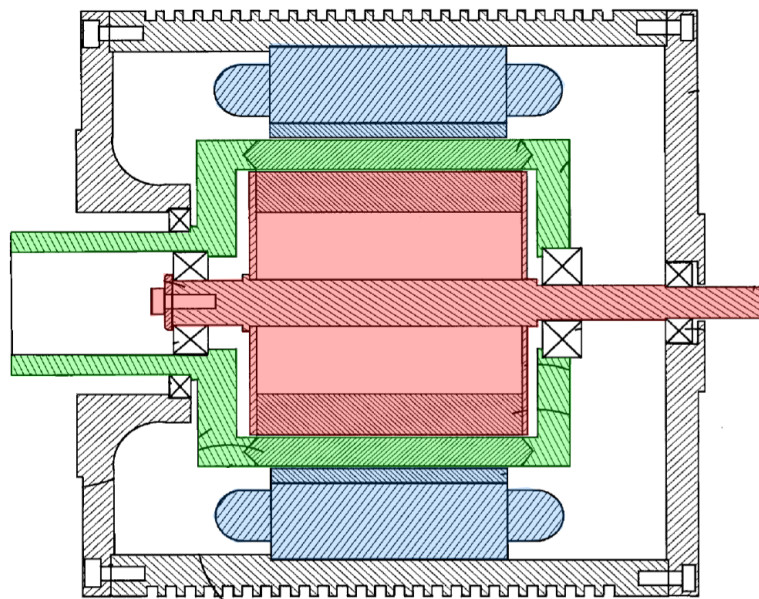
Extrait du brevet [4] : en rouge, rotor haute vitesse, en vert, les pièces polaires et en bleu, le rotor basse vitesse
